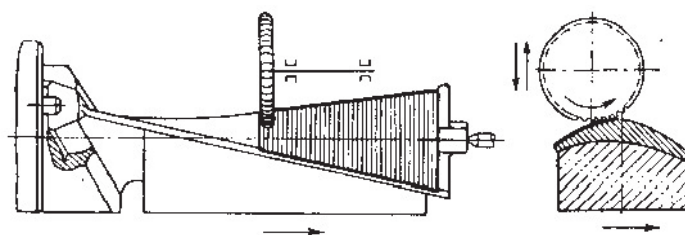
Схема роздільного фрезерування корита і спинки пера лопатки вузькими поперечними строчками.
